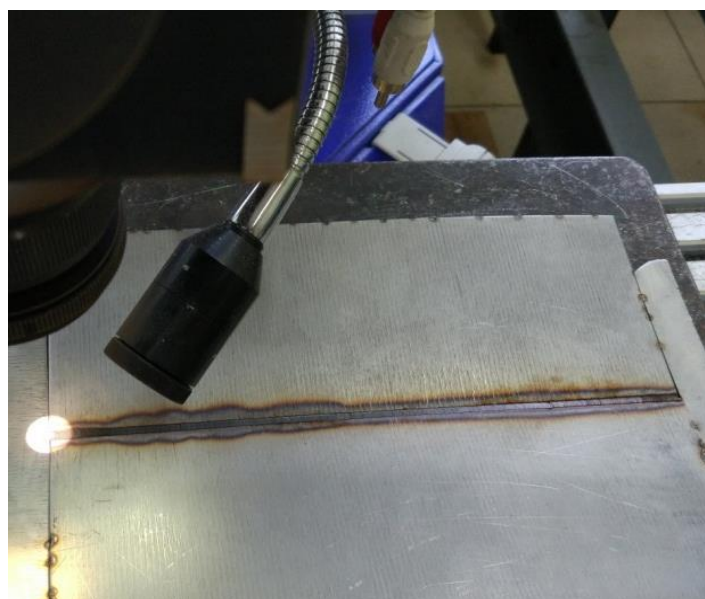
Процесс сварки стали 12Х18Н10Т толщиной 1 мм
